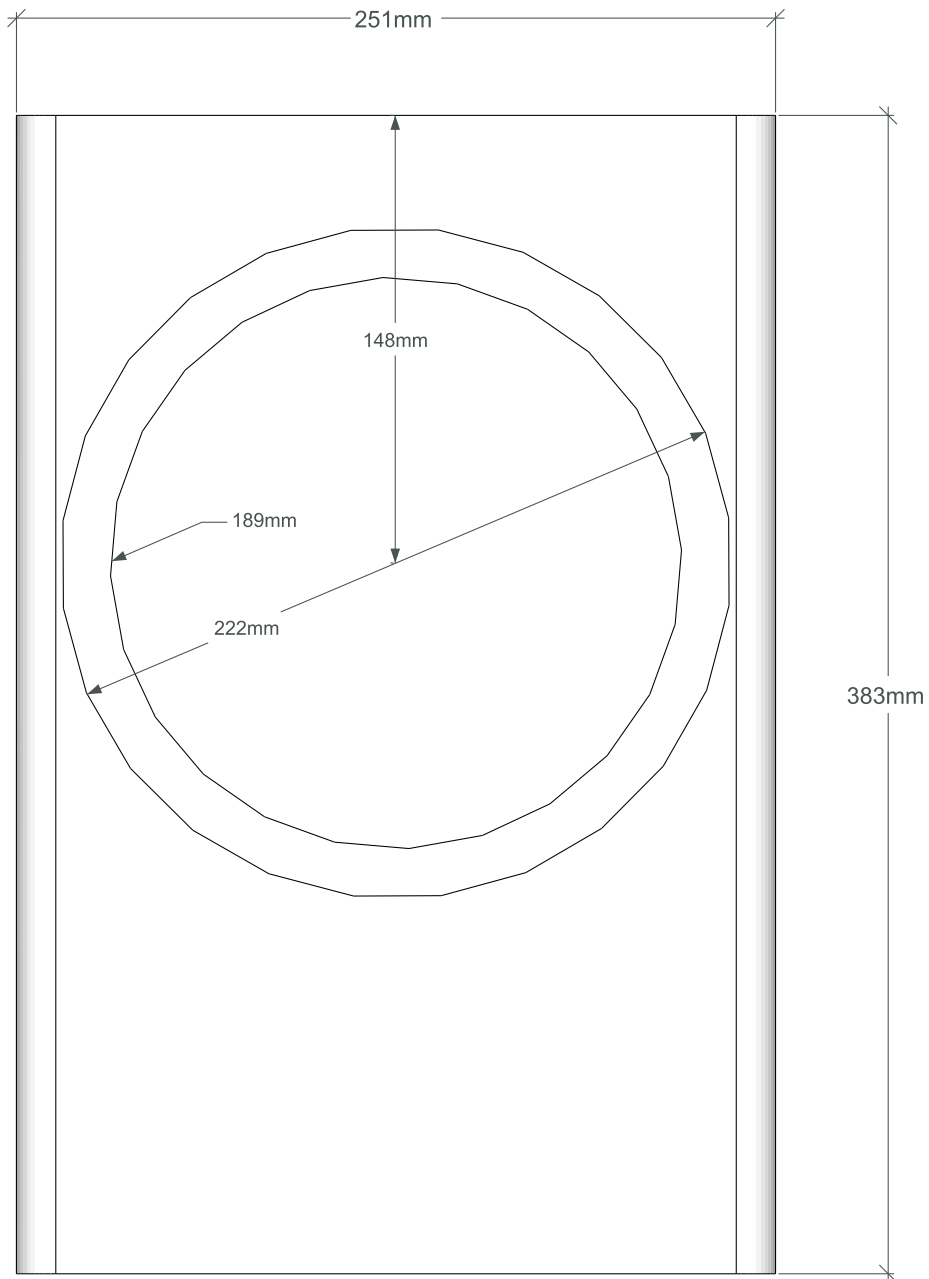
Frontansicht geschlossenes 9,7l Gehäuse
